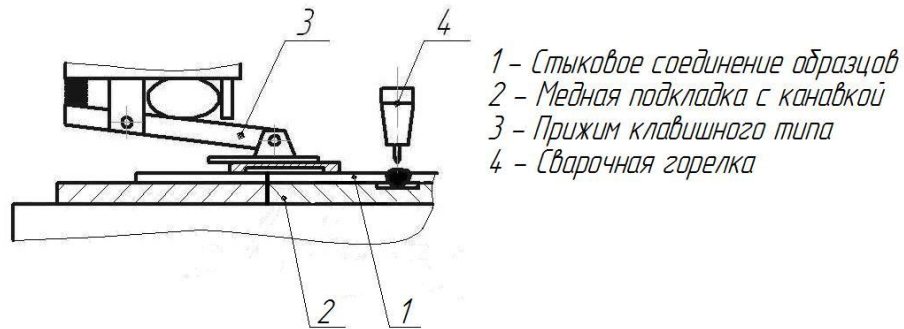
Схема закрепления образцов при сварке
